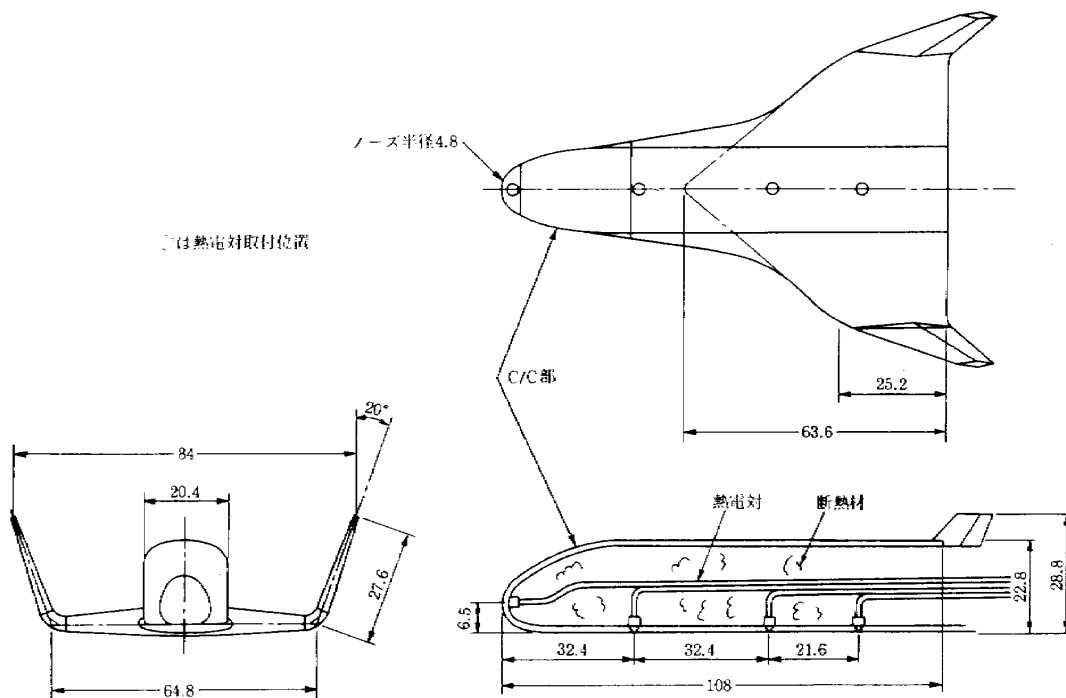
全機モデル構造及び熱電対配置図(単位: mm)
